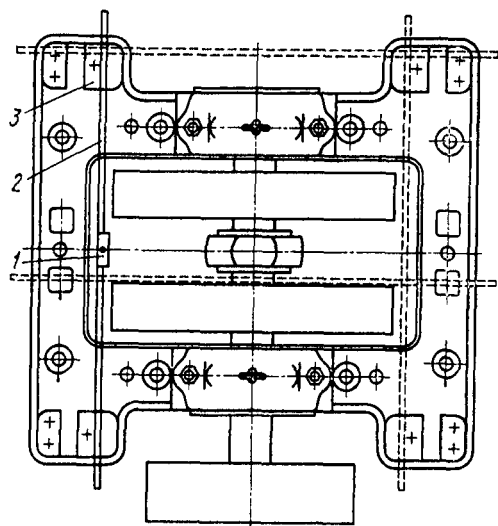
Схема выверки фундаментной плиты лесопильной рамы:
